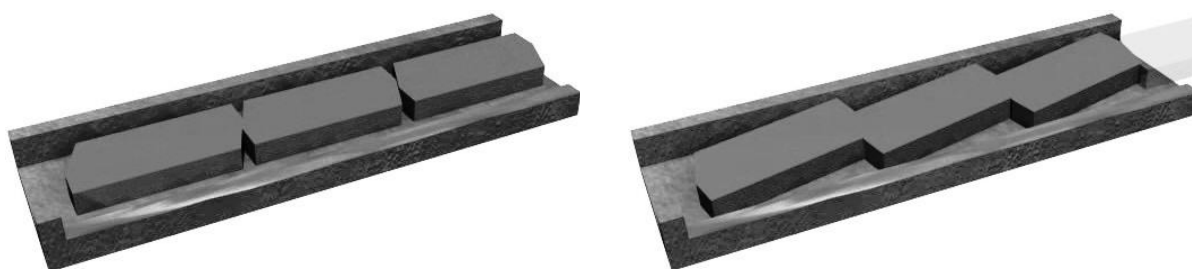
Заклинювання деталей при транспортуванні в ТЛ
